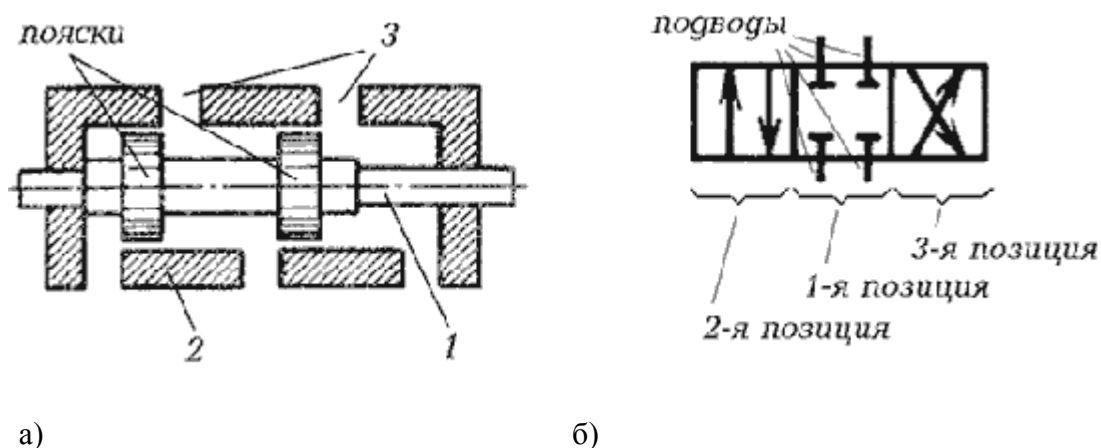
Схема (а) и обозначение (б) гидрораспределителя
